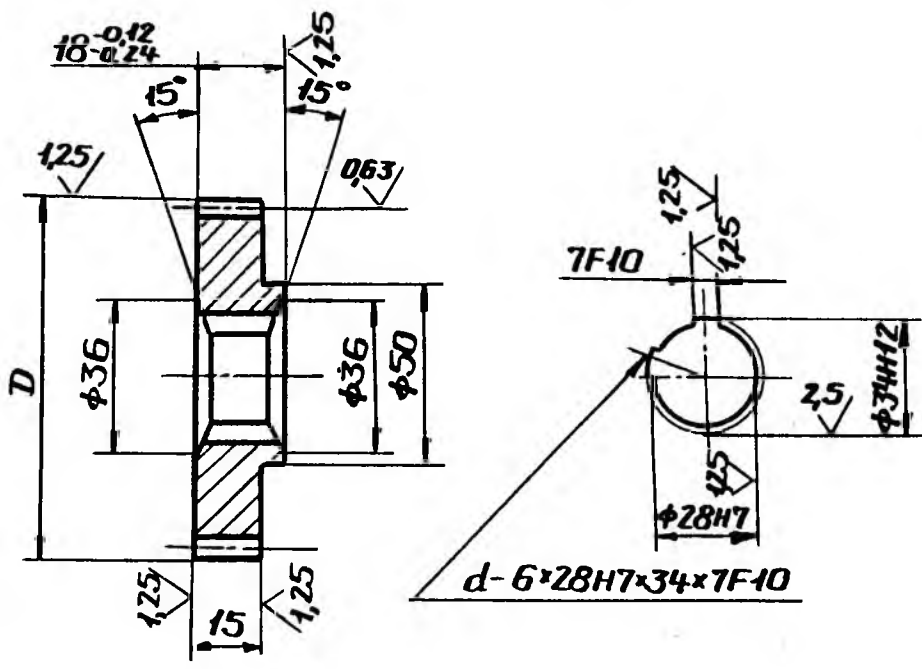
Типовой чертеж сменного зубчатого колеса.
